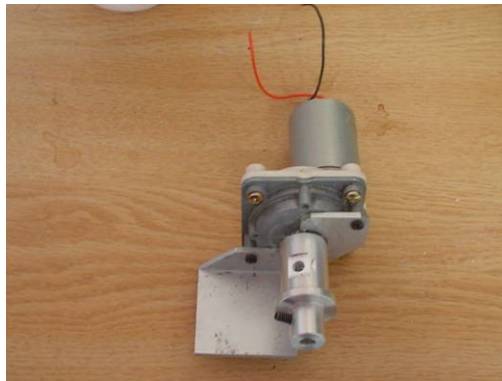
24 Adaptación cilíndrica acoplado a motor de 24v.
